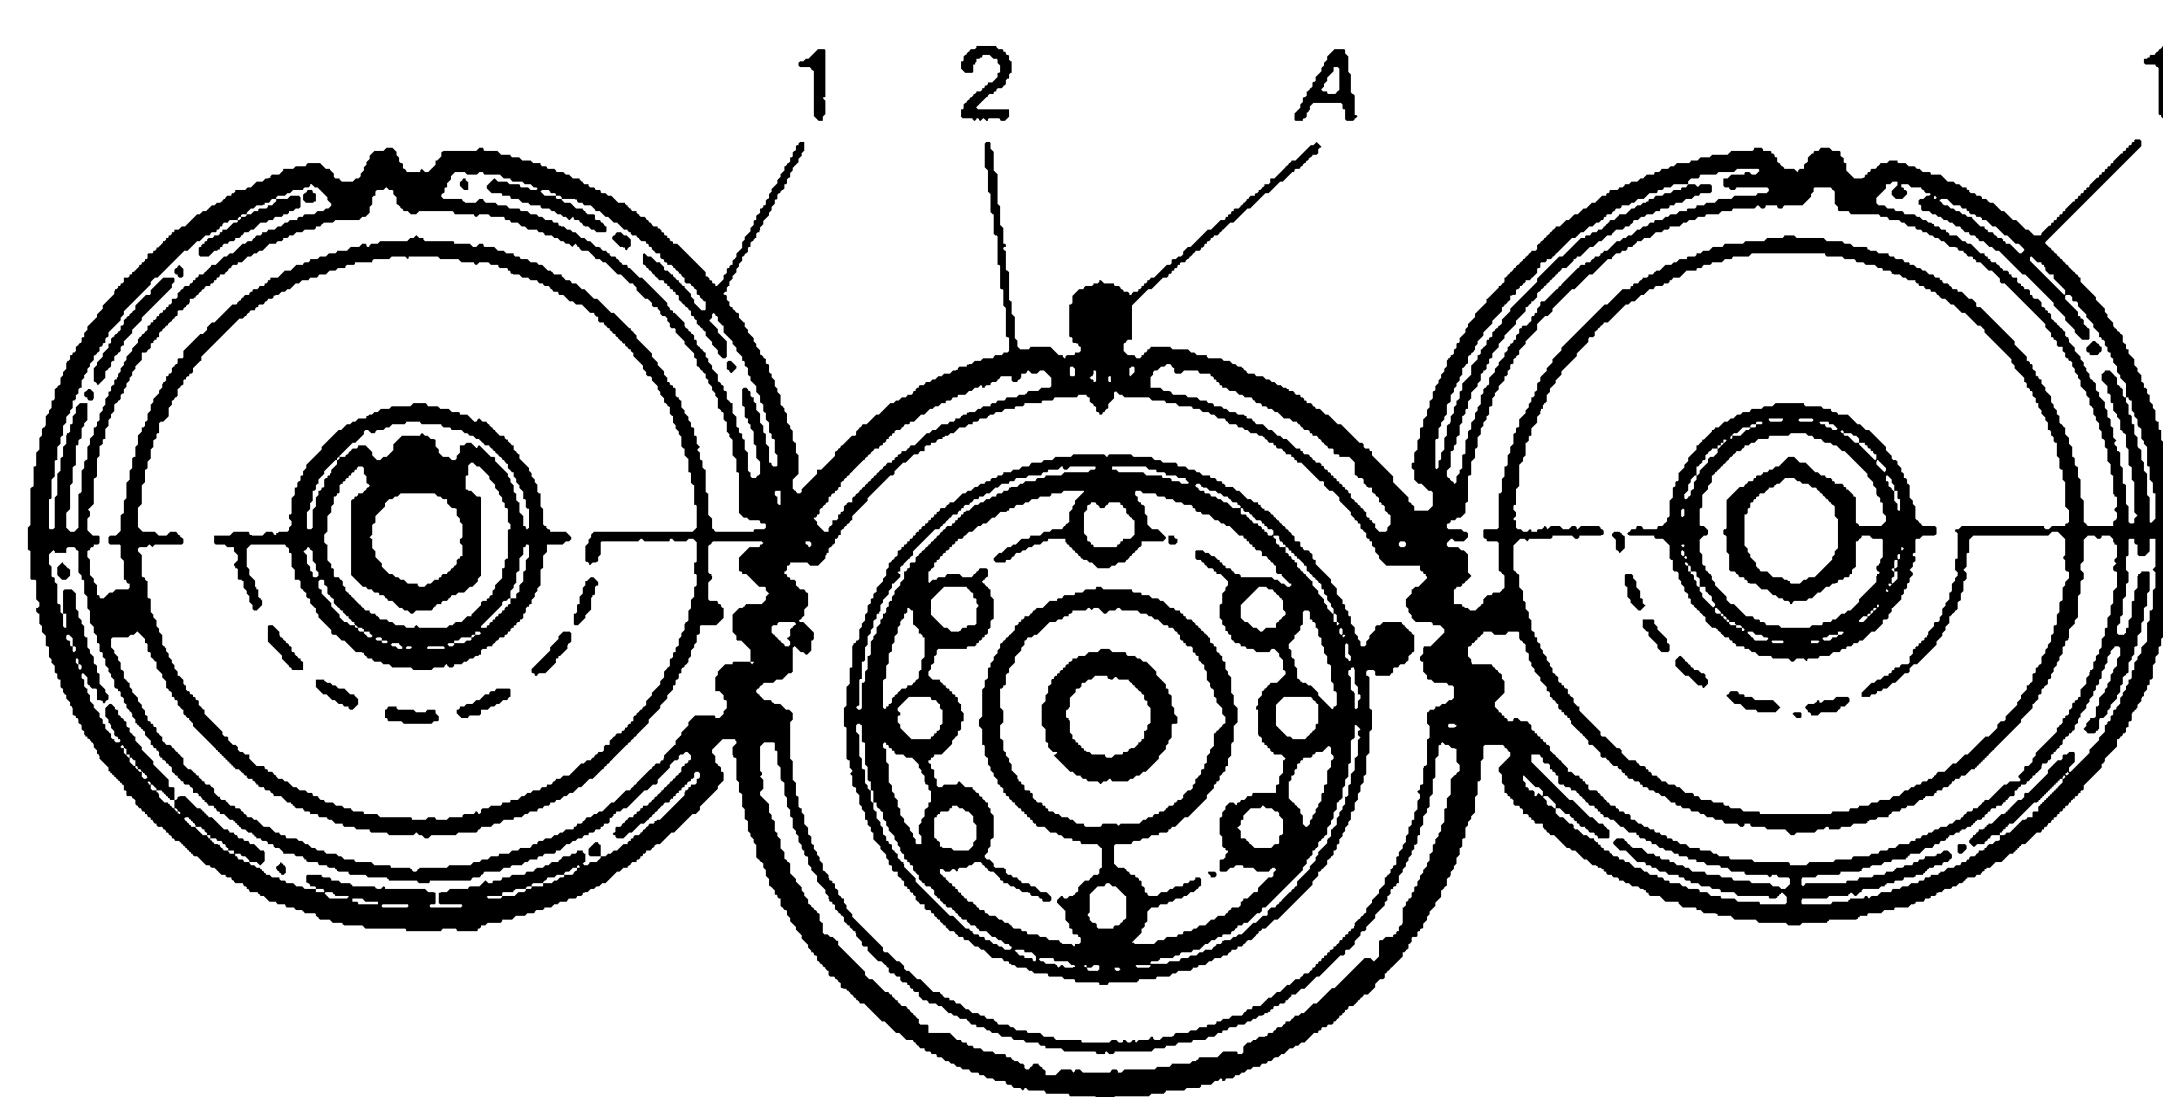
Шестерни уравнивающих валов (1) и шестерня коленвала (2); А — метка на держателе заднего сальника коленвала
